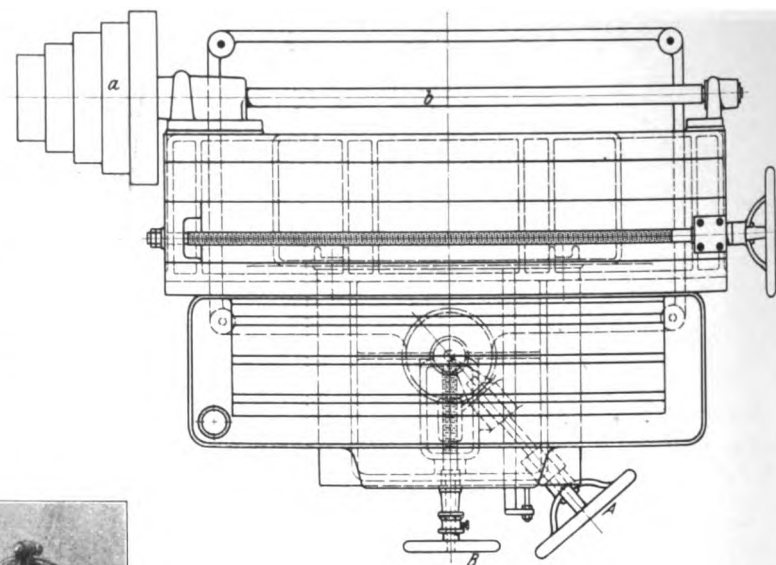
bis 174. Keilnuten-Fräsmaschine von de Fries & Co.
